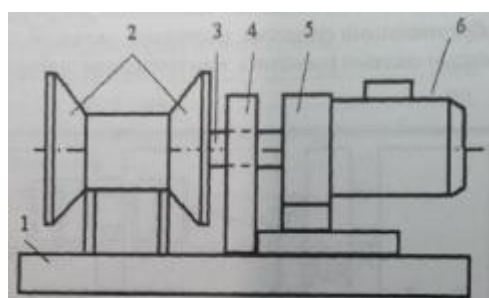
Привод продольного перемещения на трубосварочной линии: 1 - основание; 2 - ролик; 3 - вал; 4 - цепная муфта; 5 - редуктор; 6 – электродвигатель
